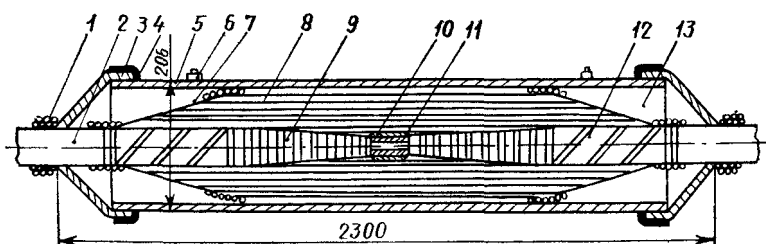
Соединительная муфта маслонаполненного кабеля низкого давления на напряжение 220 кВ: 1 – усиливающий проволочный бандаж; 2 – оболочка кабеля; 3 – раструб; 4 – пайка; 5 – корпус муфты; 6 – болт заземления; 7 – сход от изоляции муфты к изоляции кабеля; 8 – изоляция муфты; 9 – разделка изоляции кабеля; 10 – соединительная гильза; 11 – токопроводящая жила кабеля; 12 – изоляция кабеля; 13 – изоляционное масло.
